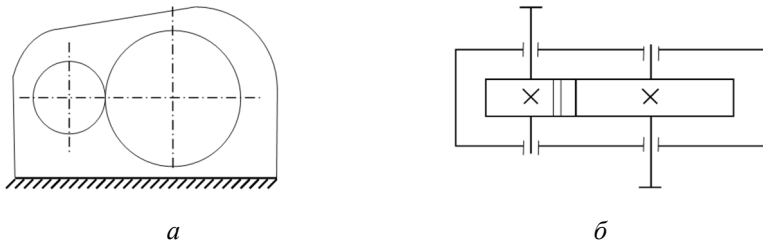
Схема редуктора: *a* – вид спереду; *б* – вид зверху
